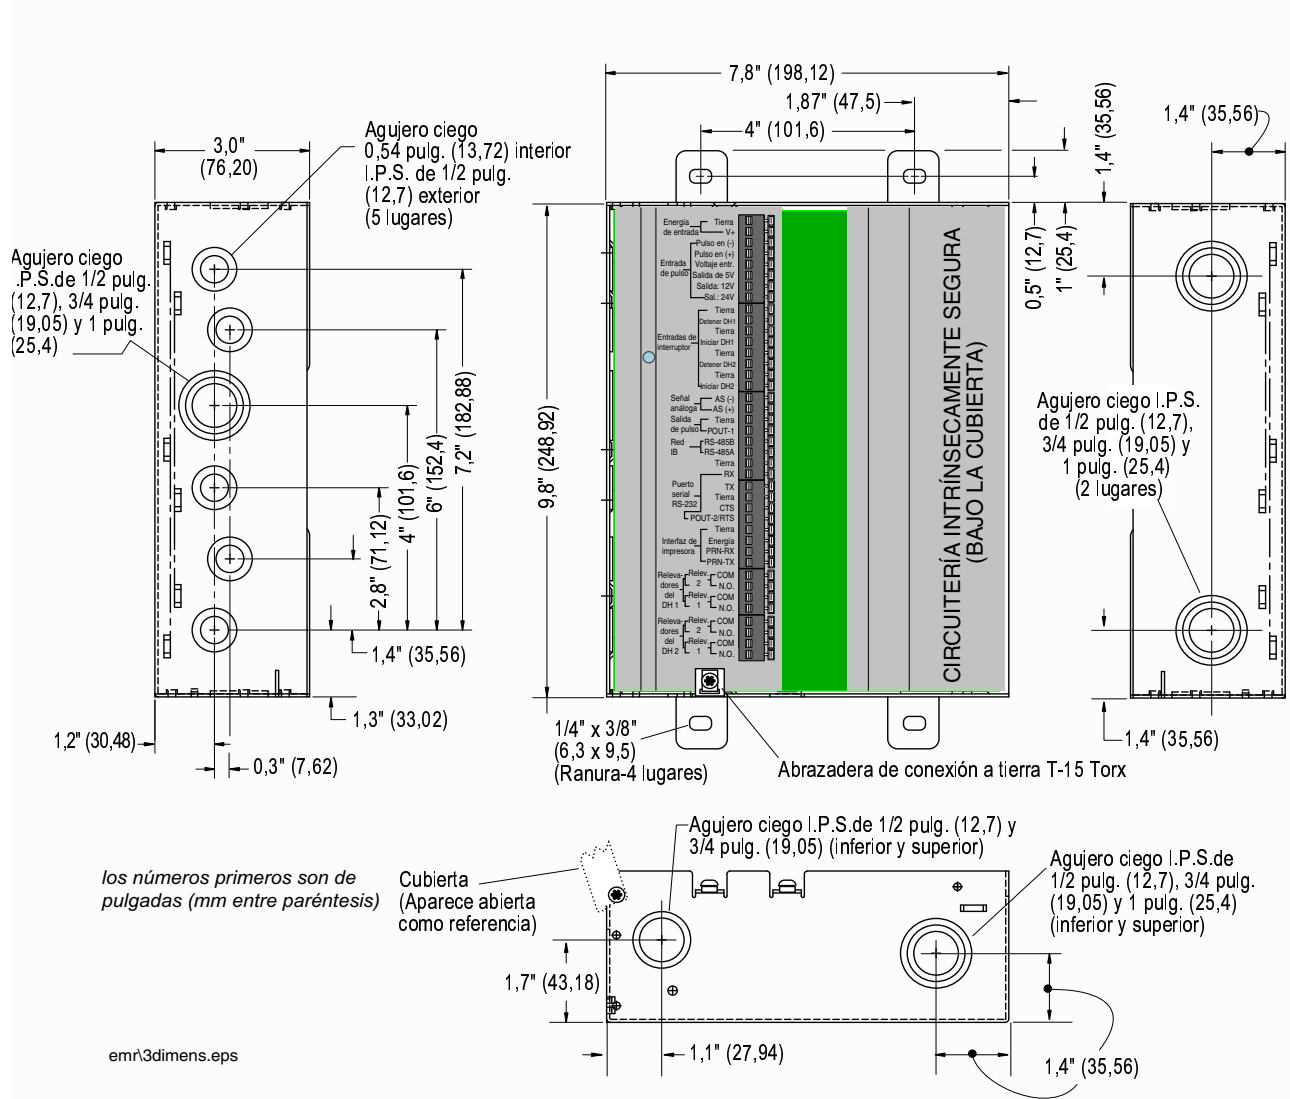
Dimensiones físicas de la IB (se muestra sin cubierta)
